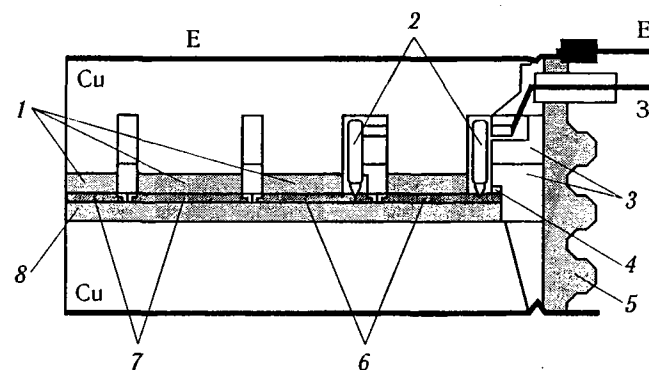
Розріз конструкції IGBT-модуля притискної конструкції: 1 — молібденові прокладки; 2 — зонди; 3 — сепаратори; 4 — рамка; 5 — керамічний корпус; 6 — чіпи IGBT; 7 — чіпи FRD; 8 — молібденовий диск
